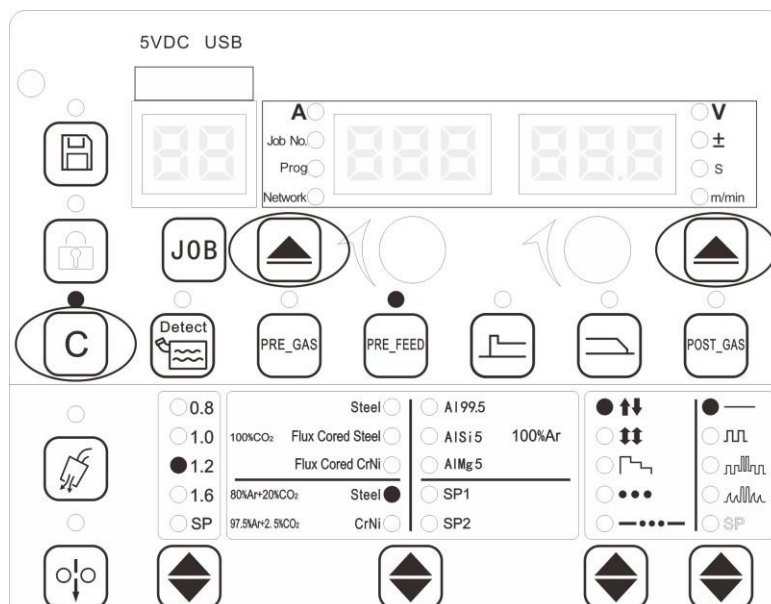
Восстановление заводских параметров источника сварочного тока
